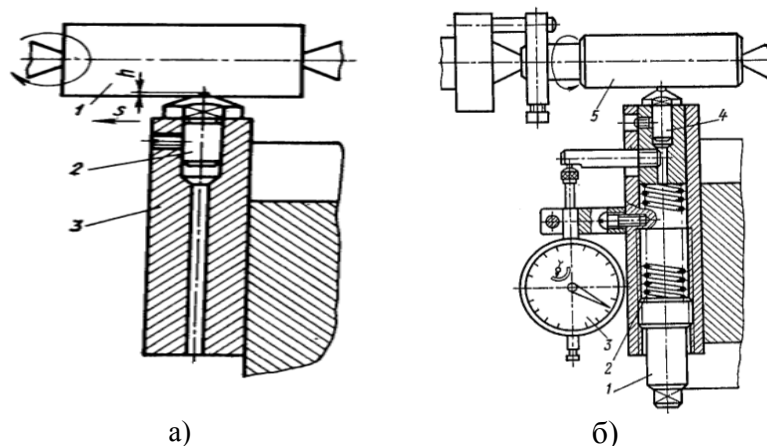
Инструмент для алмазного выглаживания: а – с жесткой и б – упругой кинематической связью между выглаживателем и обрабатываемой поверхностью
